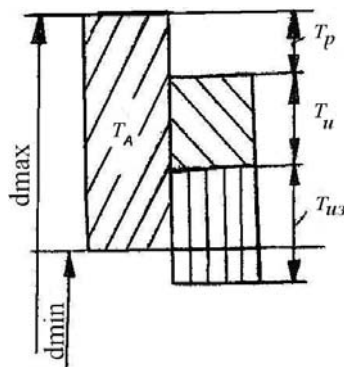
Схема расположения допусков на диаметр развертки
